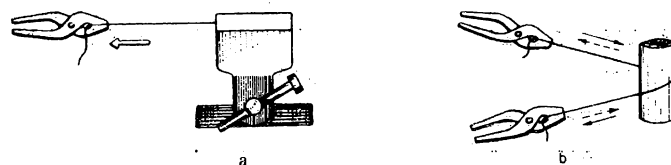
a — îndreptarea sîrmei de aluminiu și cupru
